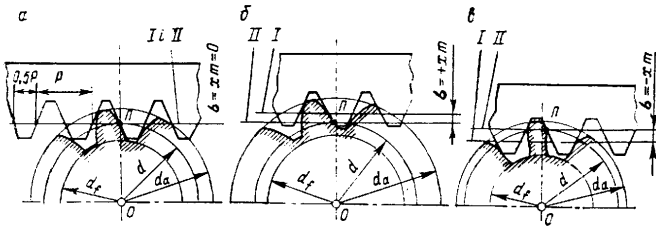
Можливі положення інструментальної рейки відносно заготовки зубчастого колеса
